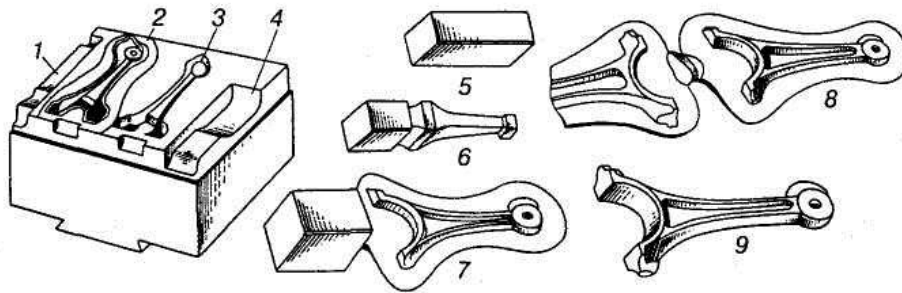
Схема штампування шатуна автомобіля: 1 – підкатний ривчак, 2 – чорновий ривчак, 3 – чорновий ривчак, 4 – попередій ривчак, 5 – вихідна заготовка, 6 – форма, 7 – поковка з облоєм, 8 – друга поковка, 9 – готовий шатун
